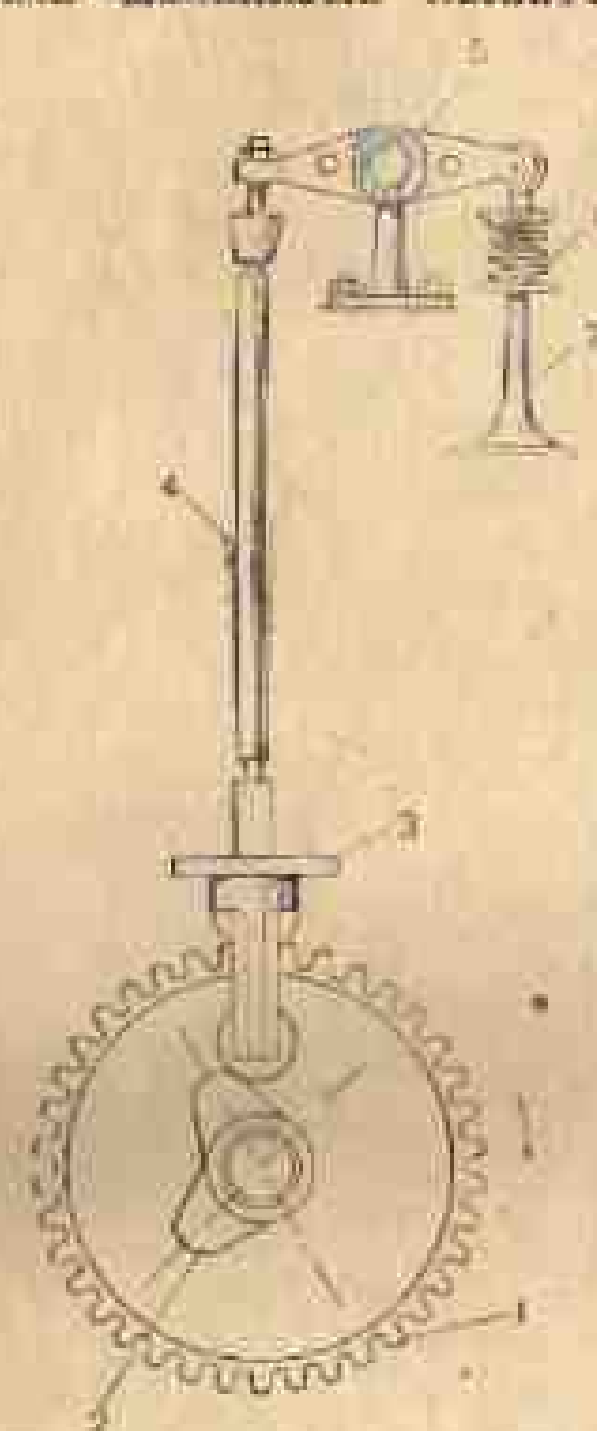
Детали газораспределительного механизма для одного цилиндра:
